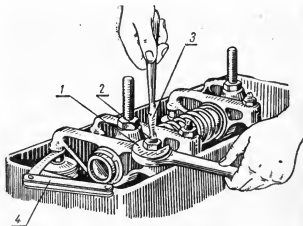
Регулировка зазора клапанов двигателей Д-54 и Д-54А:
